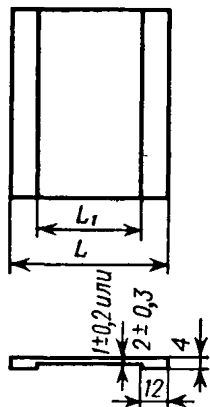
Форма и размеры пластин для вырубki образцов с напльвами.
